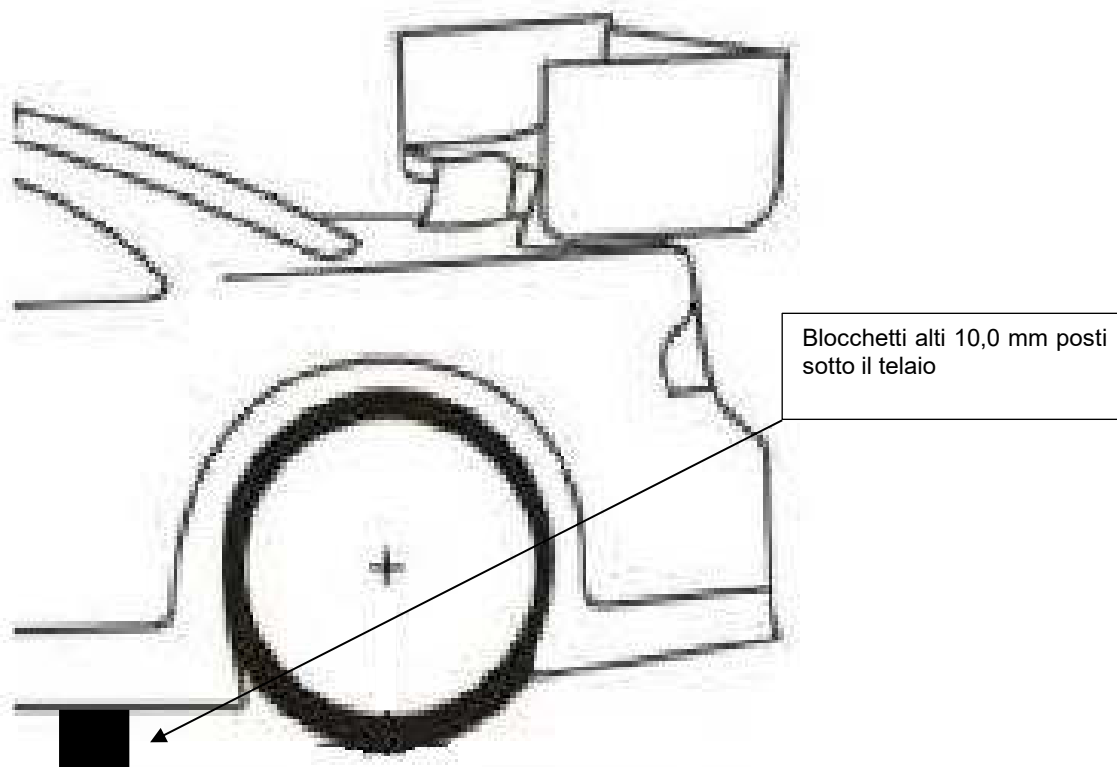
Disposizione blocchetti da 10 mm sotto il telaio
